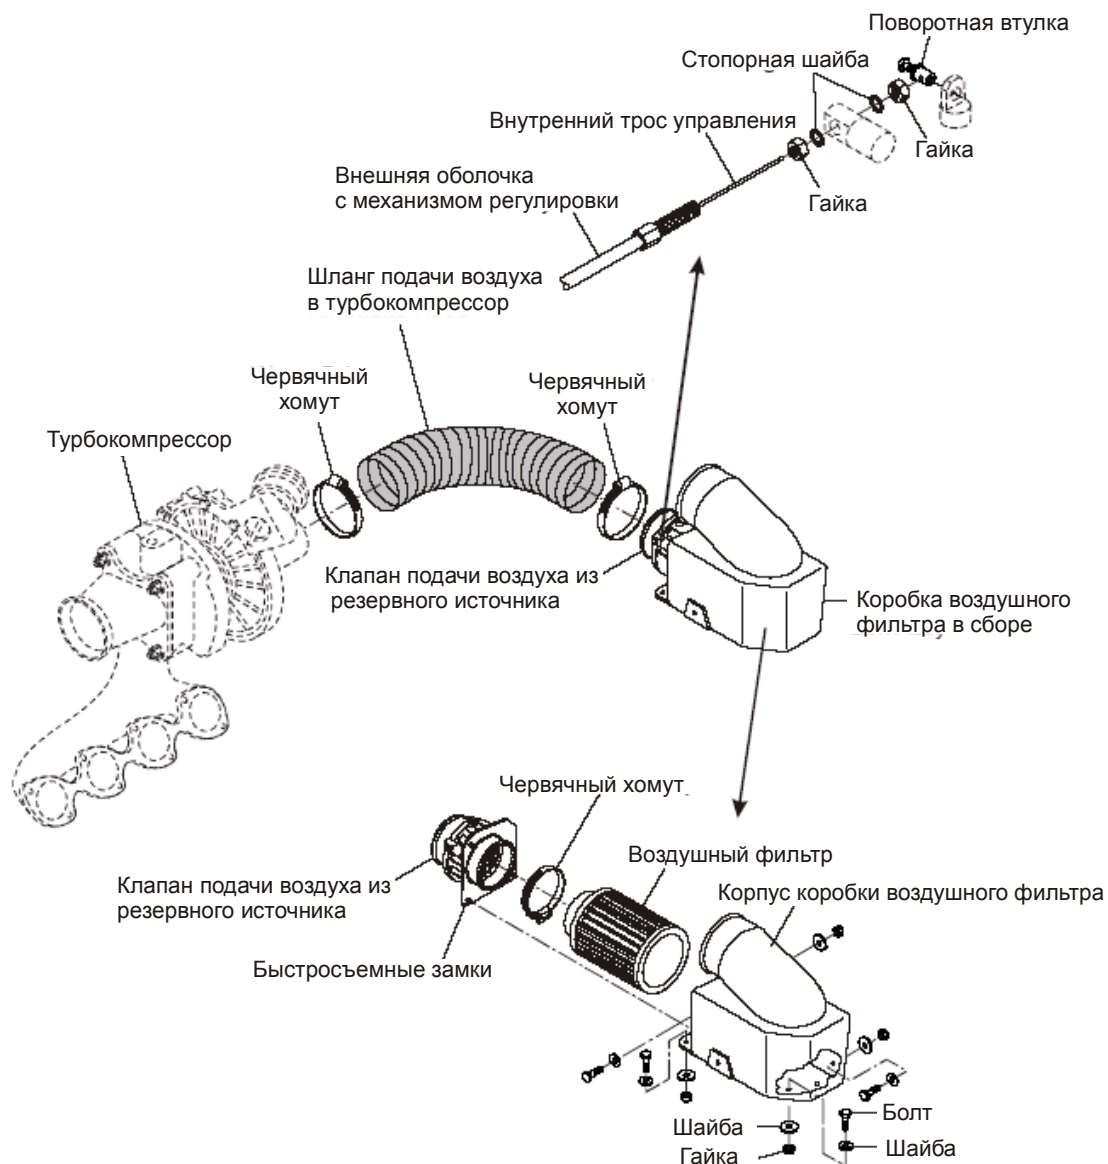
Воздушный фильтр и клапан подачи воздуха из резервного источника
